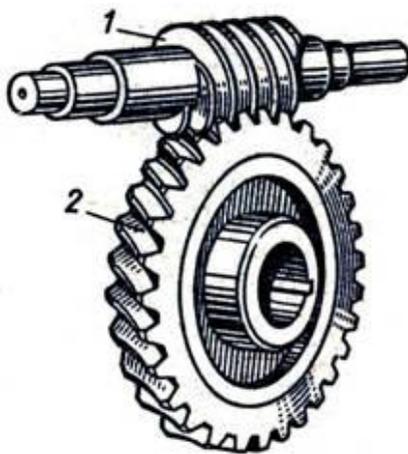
Червячная передача: 1 - червяк и 2 - червячное колесо с зубьями особой формы
